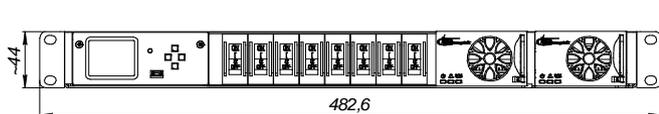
Габаритный чертеж УЭПС-7К 48/74 (60/60)-22-Т
